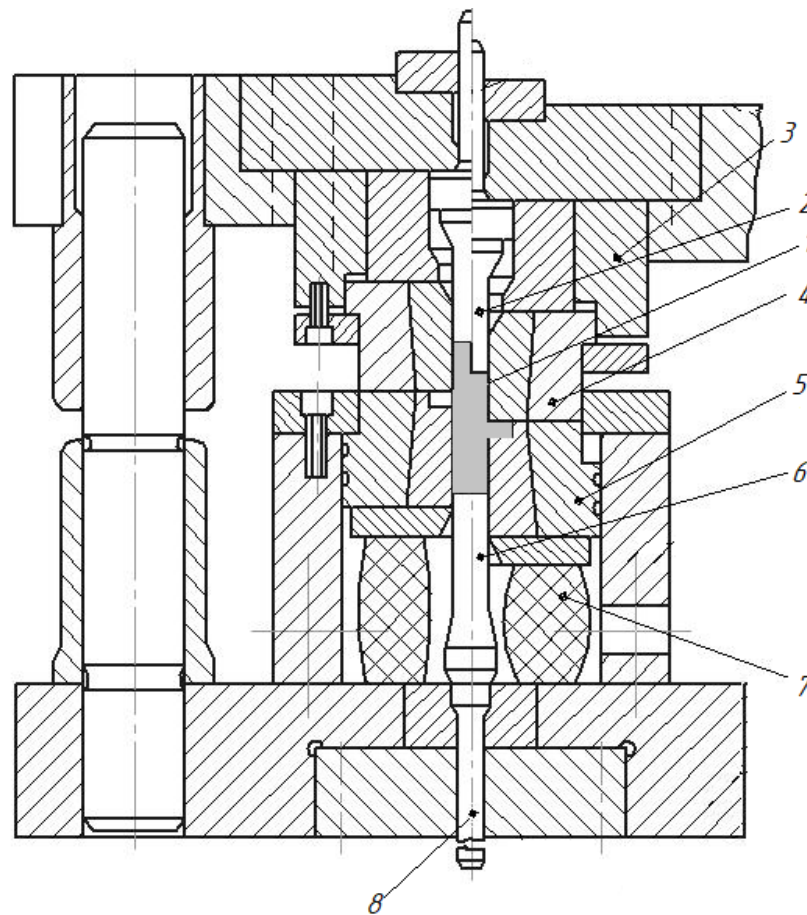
Штмп для радіального видавлнювання деталі з фланцем
